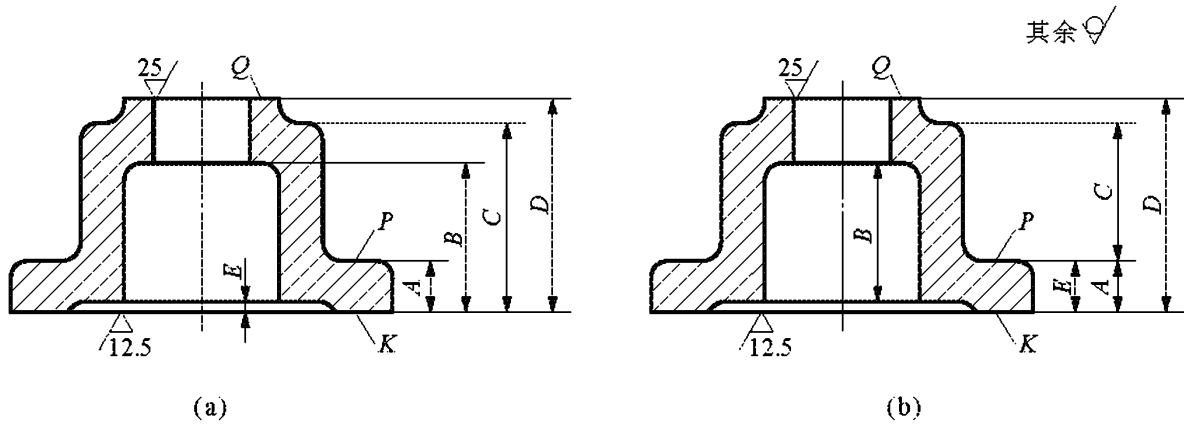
多个加工表面与不加工表面之间的尺寸标注
